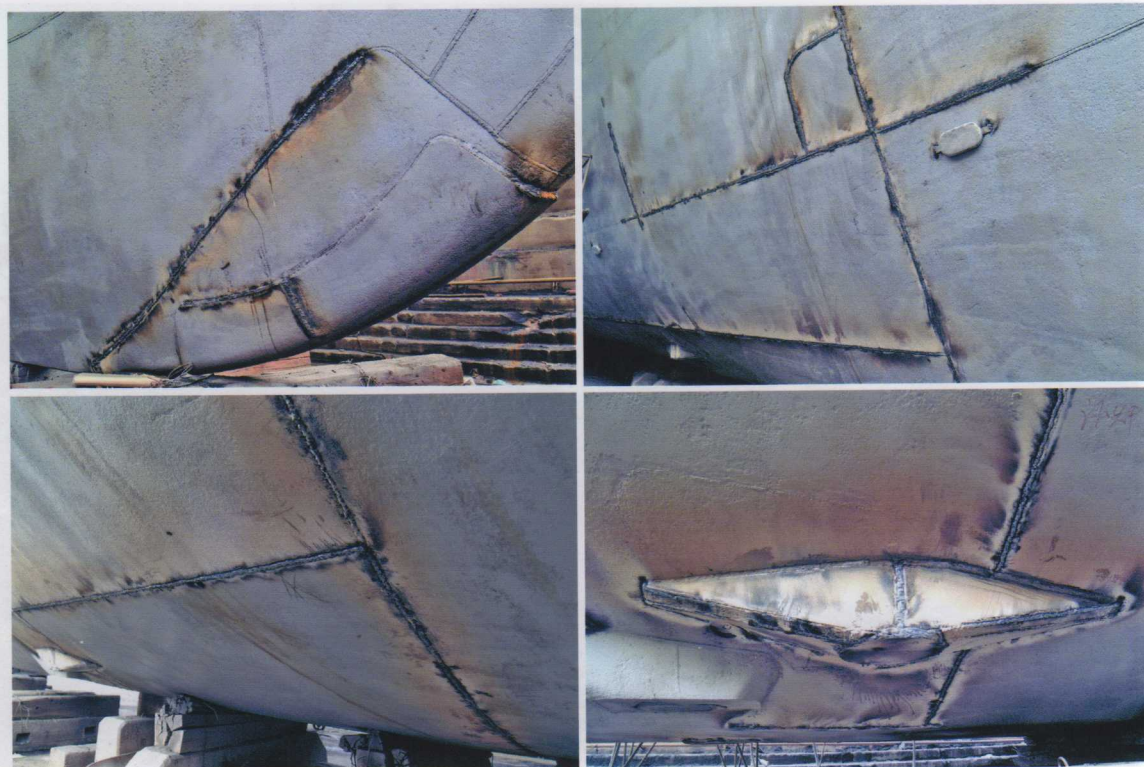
21. Сварные швы наружной обшивки корпуса судна после наплавления.
